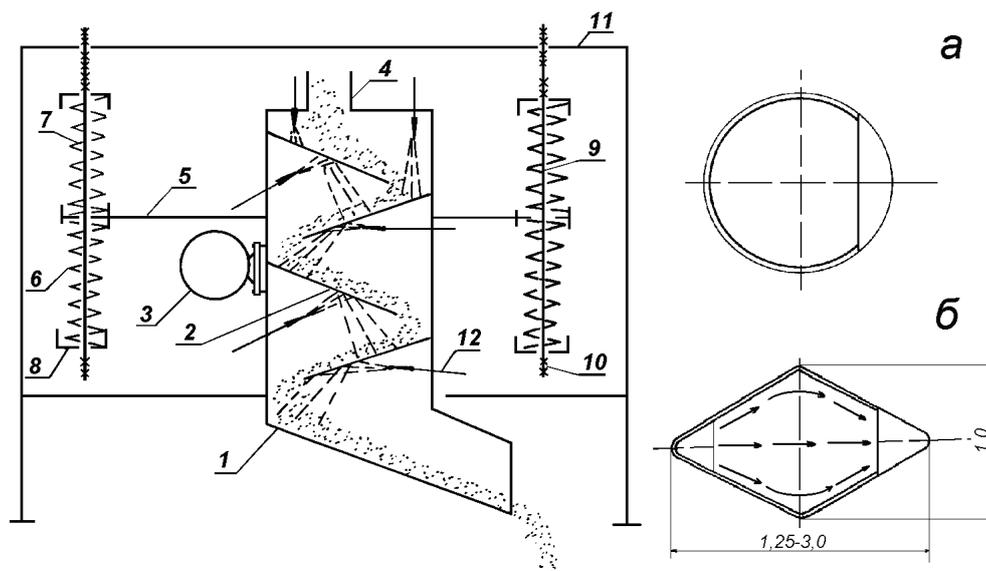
Принципиальная схема установки вибрационного смесителя-увлажнителя пыли: 1 – корпус; 2 – наклонные полки; 3 – электромеханический вибратор; 4 – приемный патрубок; 5 – балка; 6, 7 – пружины; 8 – стаканы; 9 – шпилька; 10 – гайка; 11 – рама.
